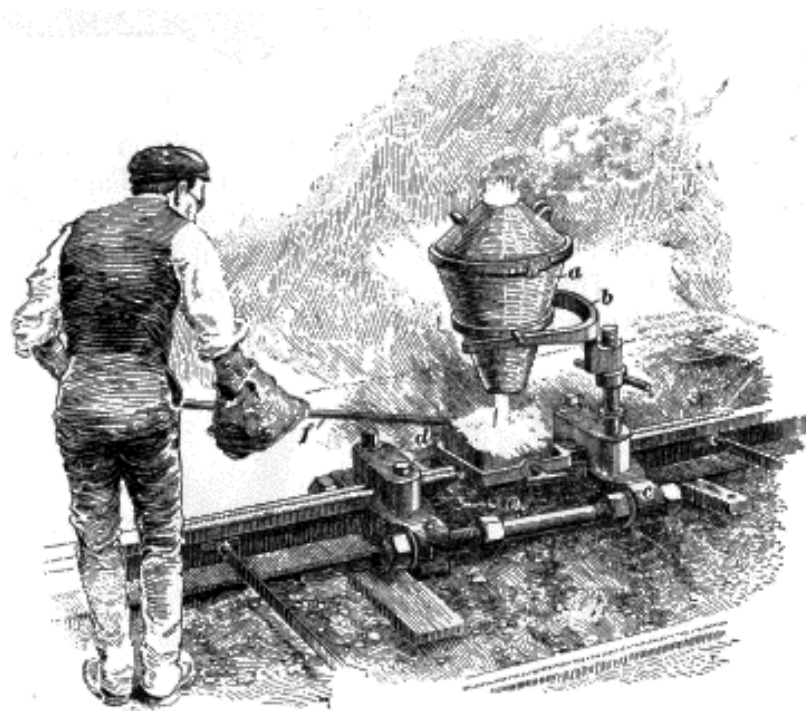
Сварка рельсов комбинированным способом
